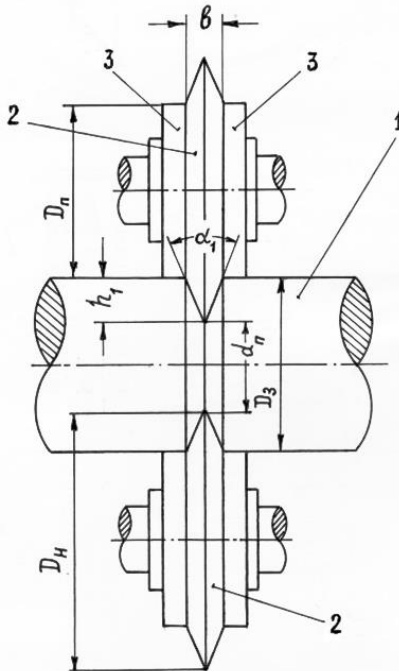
Перша стадія розділу гарячої заготовки дисковими ножами: 1 – заготовка; 2 – дисковий ніж; 3 – деформуючий пояснок ножа.
